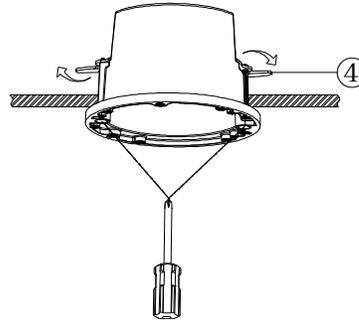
COLOCACIÓN DE LA PLANTILLA
